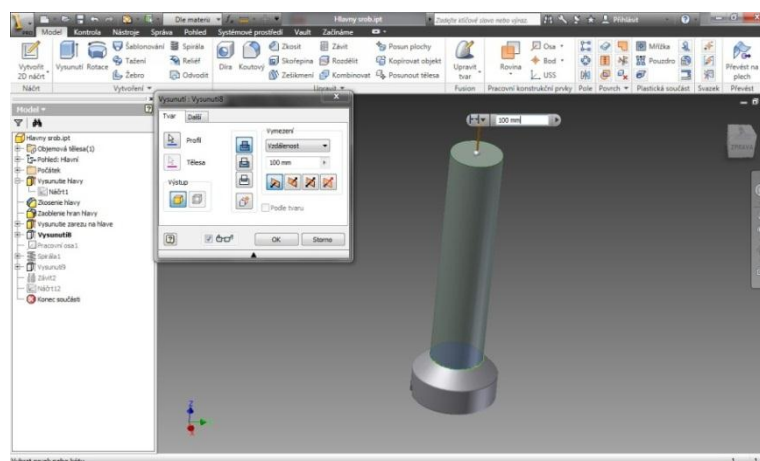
Tvorba hlavy hlavnej skrutky
